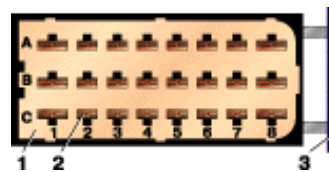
Разъем жгута проводов системы управления двигателем: 1 – корпус разъема; 2 – штекерный контакт; 3 – стопорная планка
